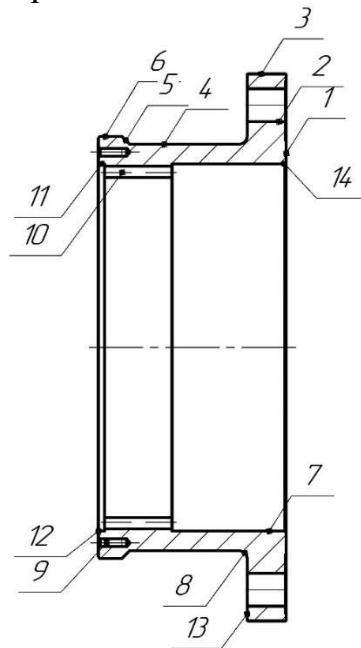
Нумерація конструктивних елементів та поверхонь деталі Обойма
